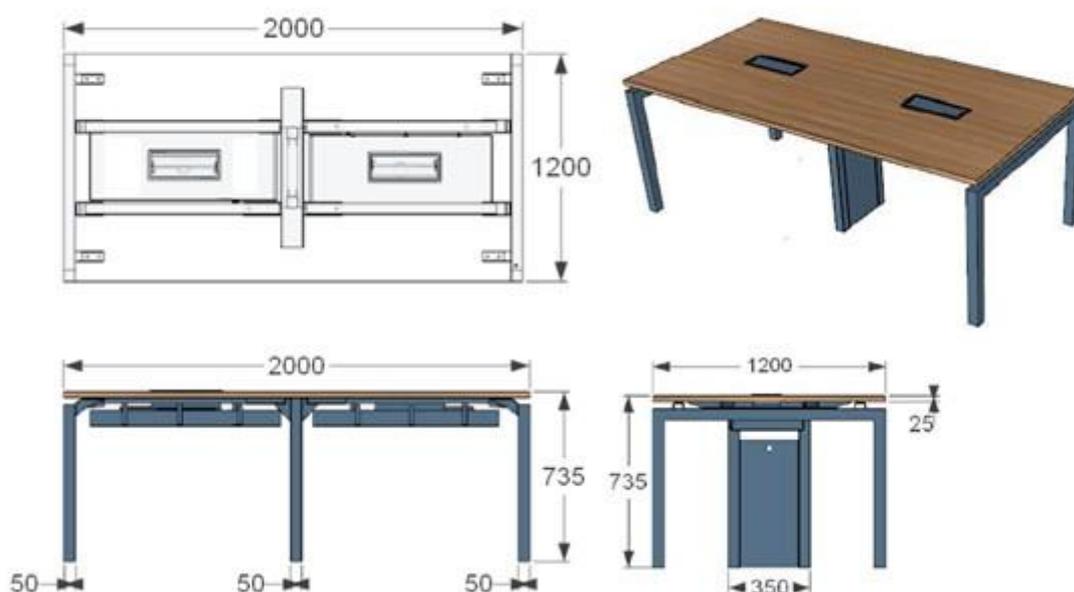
Planta baixa, vista frontal, vista lateral e perspectiva modelo item 21
